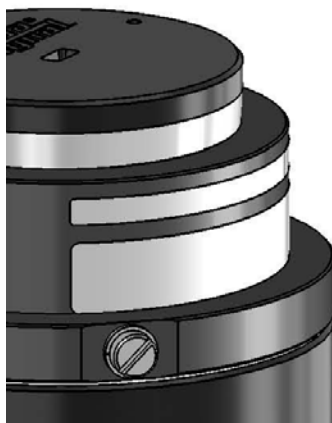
Kontaktieren mittels Schraubendrehers
